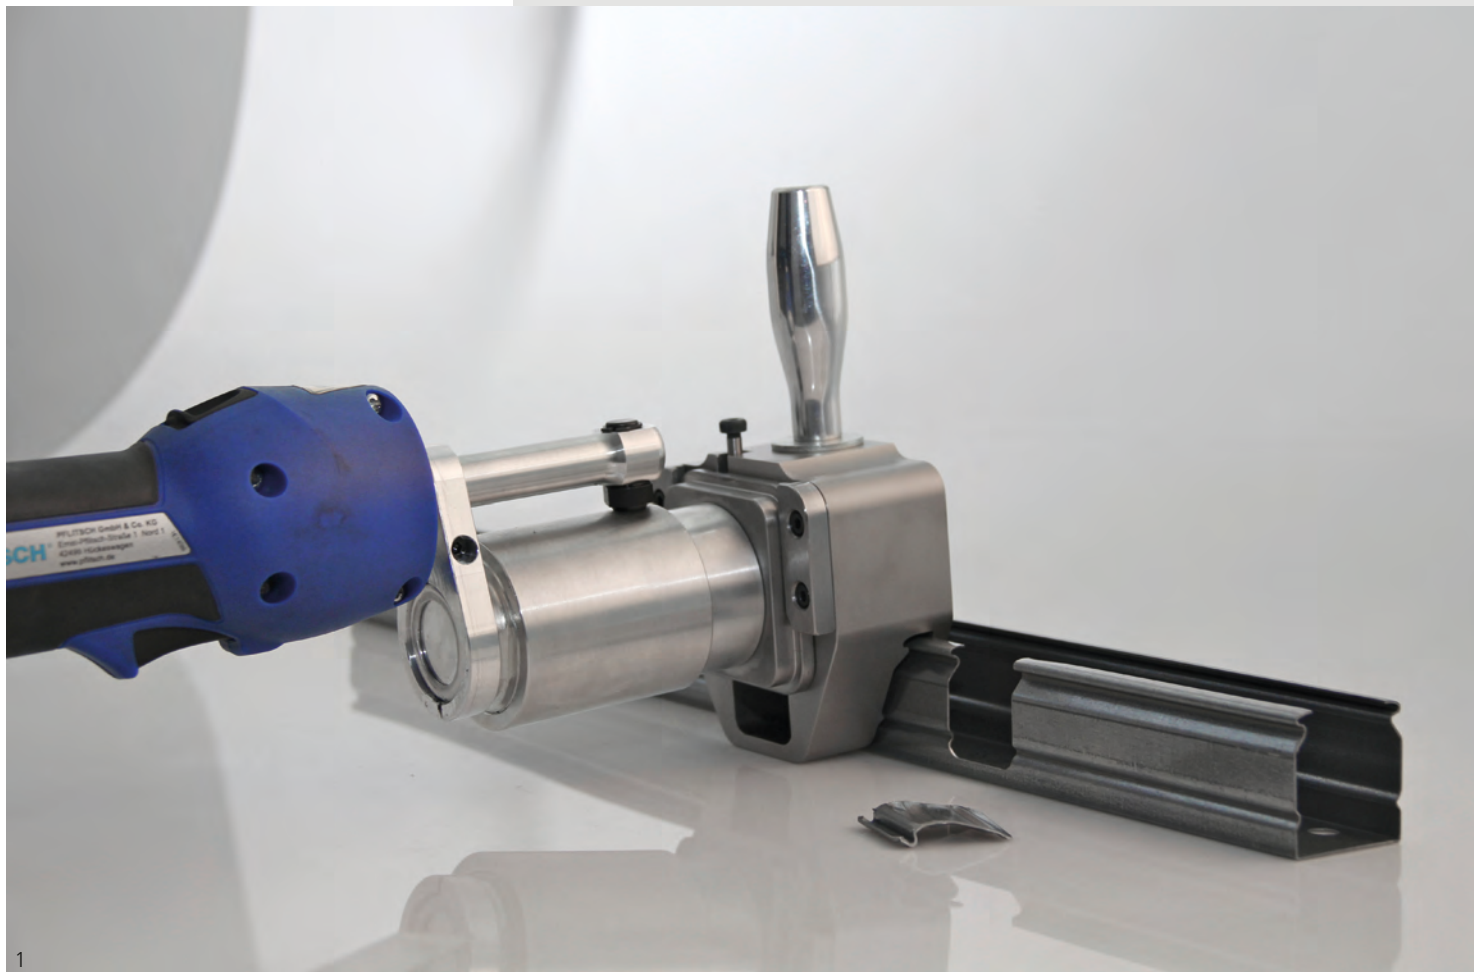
Ausklinkwerkzeug für PIK-Kanäle
